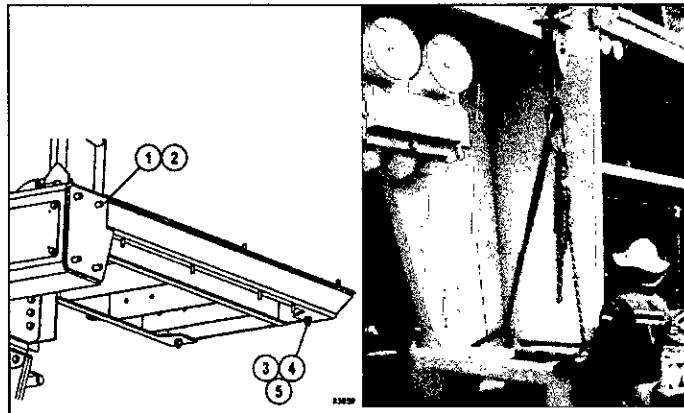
Soldadura de soporte derecho de filtros
